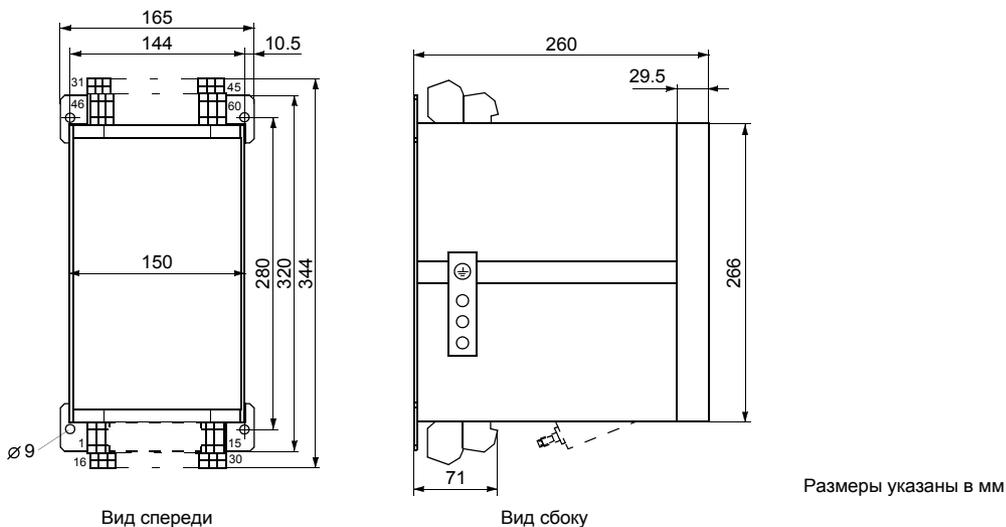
Размеры устройства 7UT612 с корпусом для навесной установки
